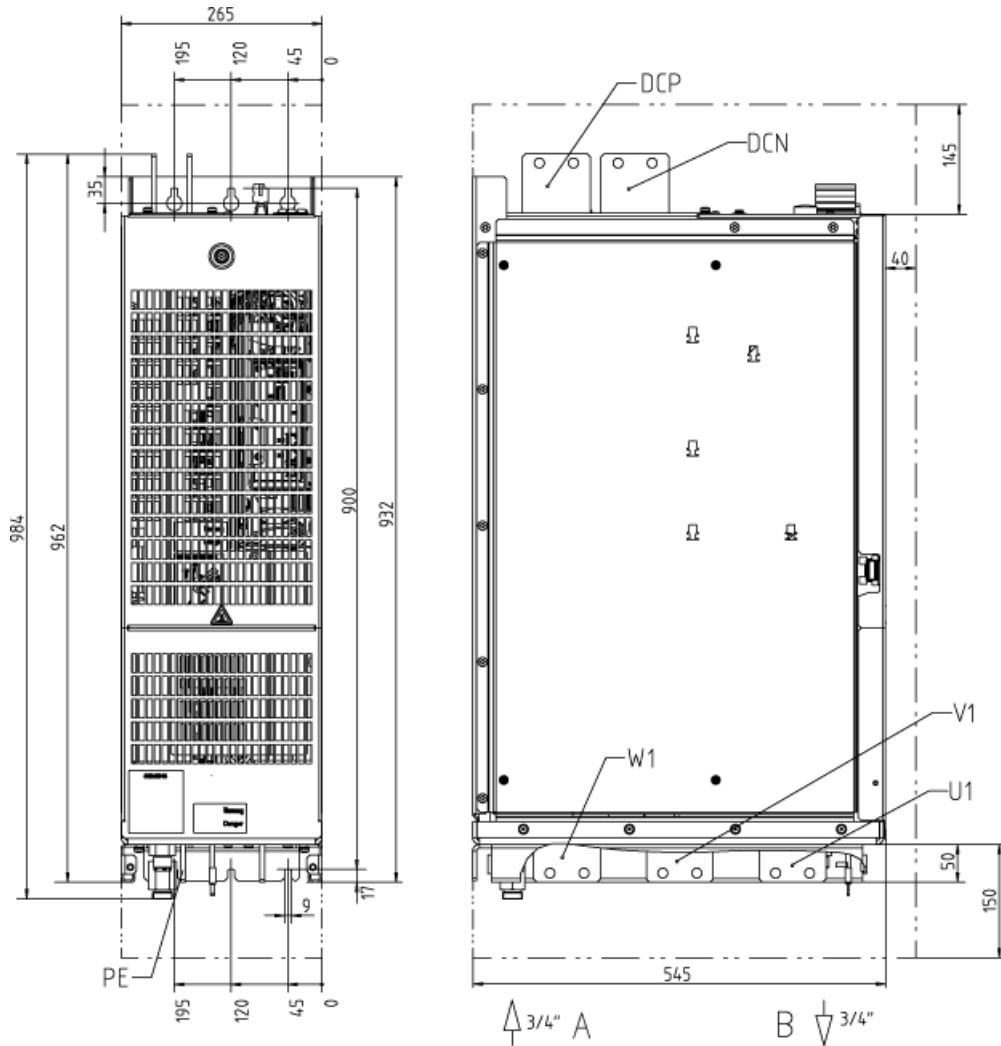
Габаритный чертеж активного модуля питания, типоразмер HXL. Вид спереди, вид сбоку
